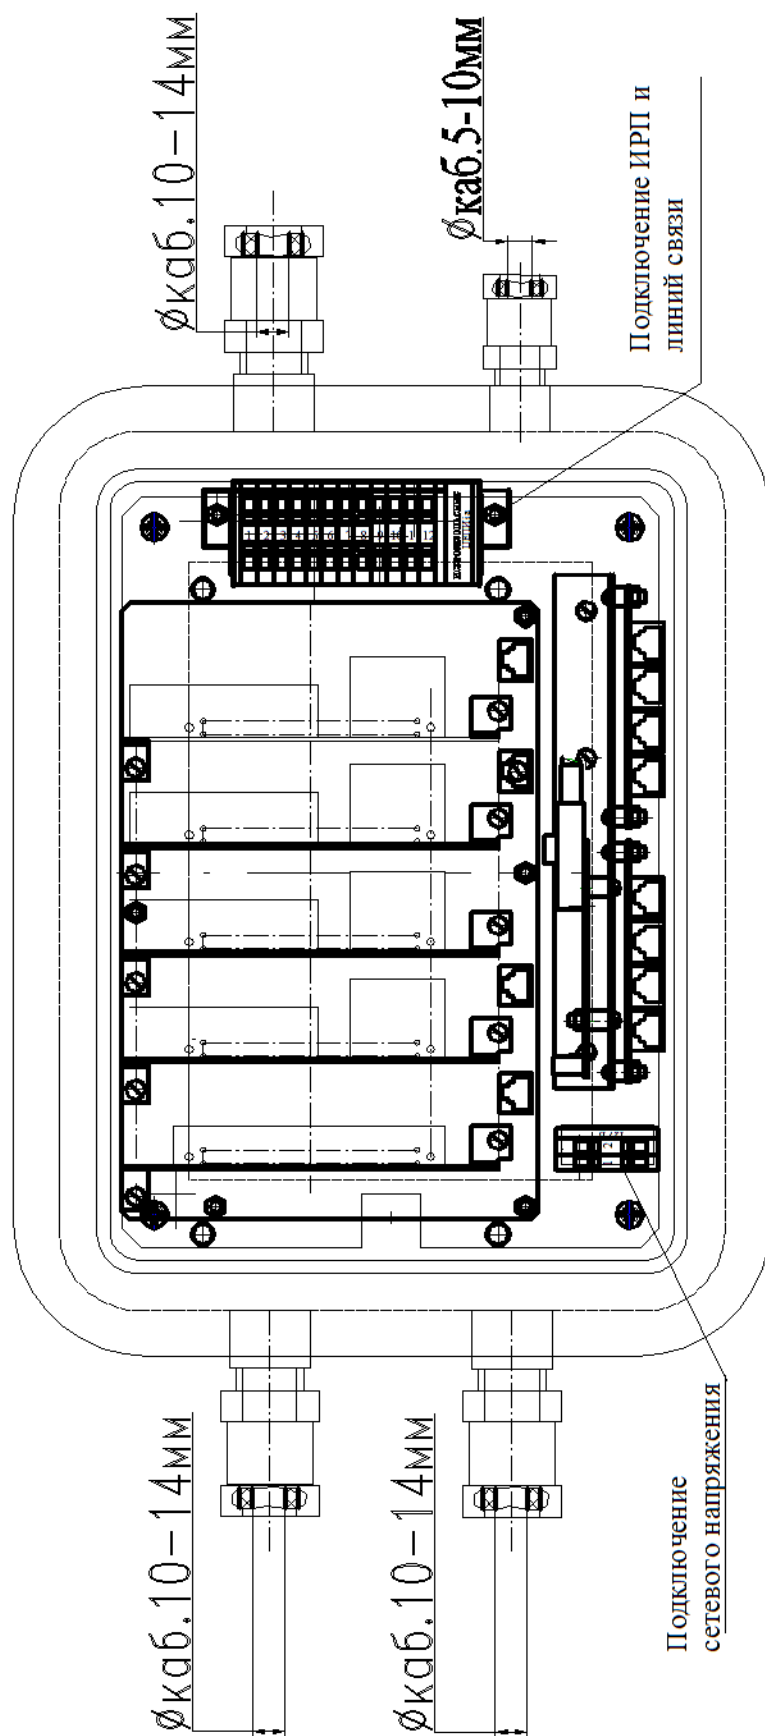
Чертёж корпуса IP-шлюза со снятой крышкой.
